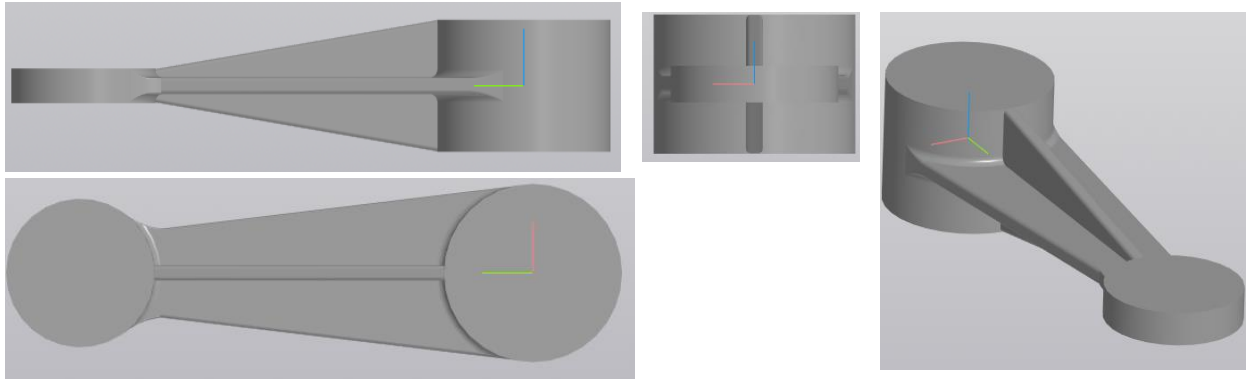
Комп'ютерна 3D- модель заготовки деталі «Качалка»
